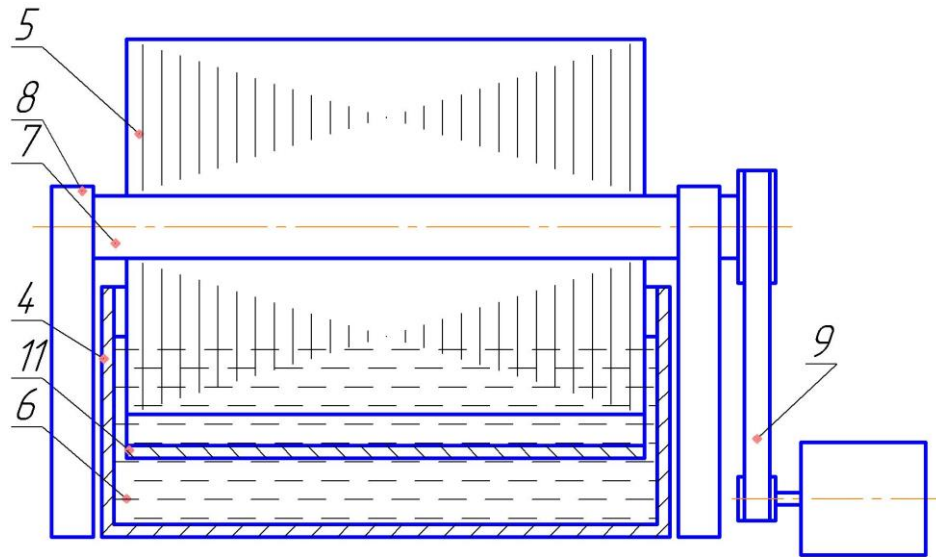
Вид спереду (в розрізі) пристрою для проведення електрохімічної обробки пошкодженої поверхні осердя короткозамкненого ротора
